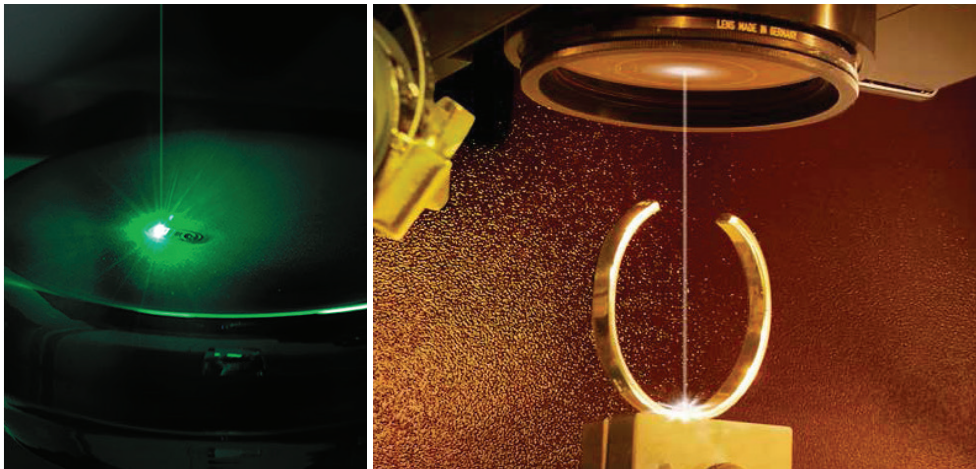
Процесс лазерного клеймения изделий из драгоценных металлов
